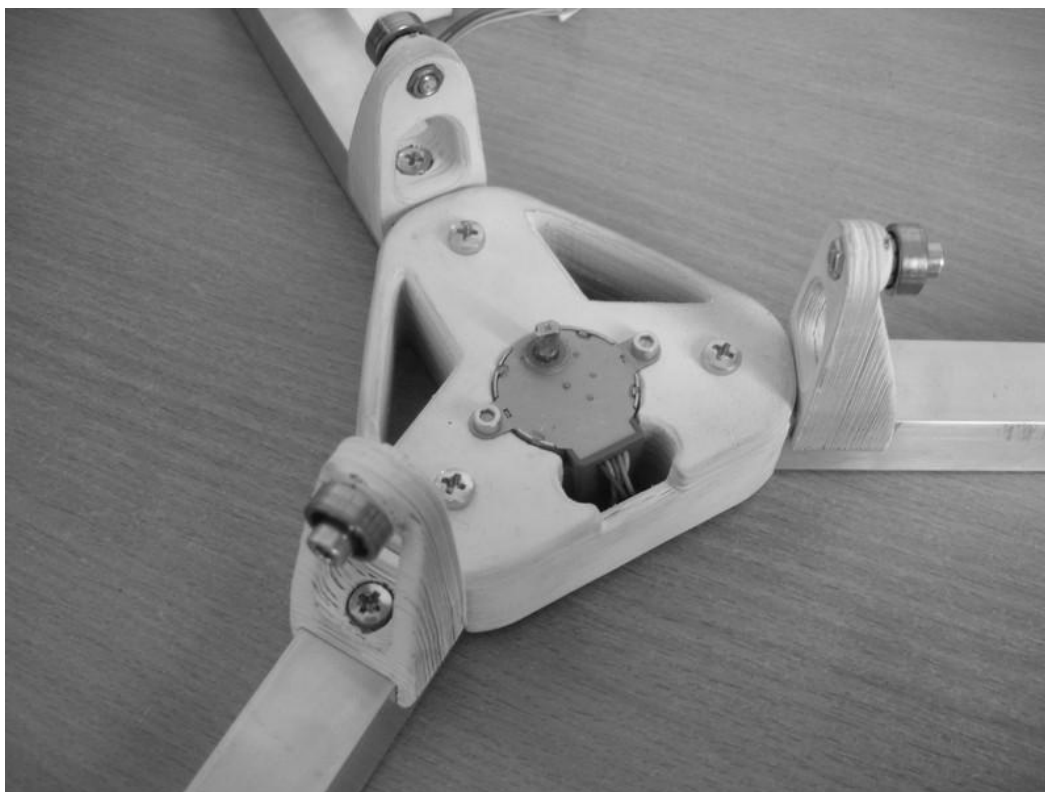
Крестовина поворотного стола и поддерживающие опоры
